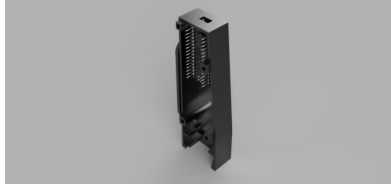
3D-модель верхней части для отражателя основного корпуса
